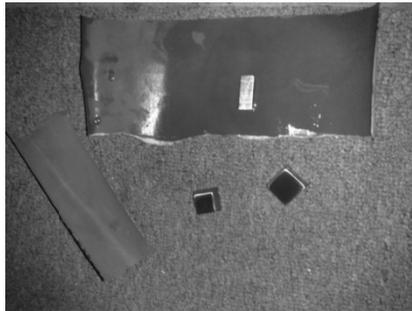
Diseño volumétrico de probeta sin soldadura
